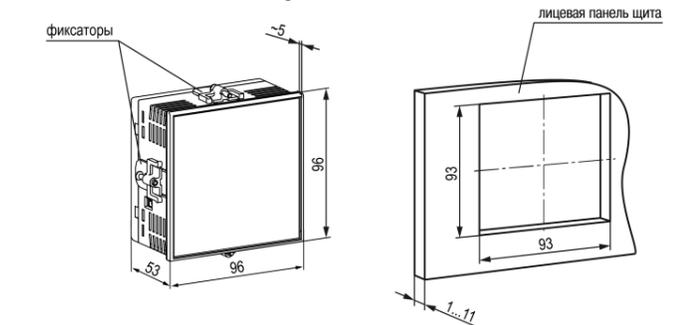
Габаритные размеры корпуса Щ1 и монтажного отверстия в щите
